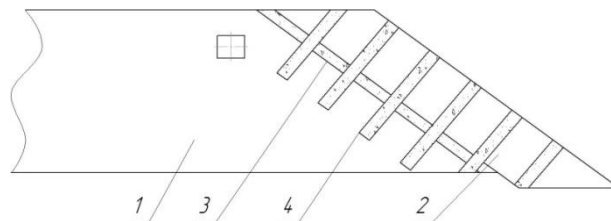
Лемех плуга для отвальной вспашки: 1 – рабочая поверхность; 2 – долото; 3 – сварной шов; 4 – армирующие валики
